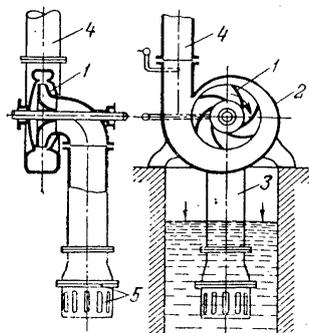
Схема центробежного одноступенчатого насоса:
